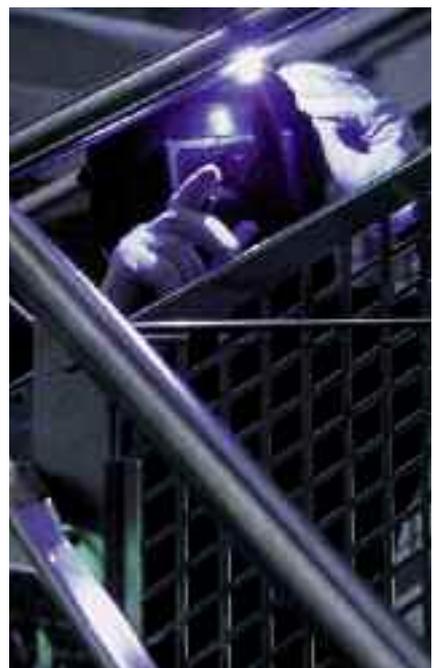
WIG-Schweißen eines Edelstahlgeländers
